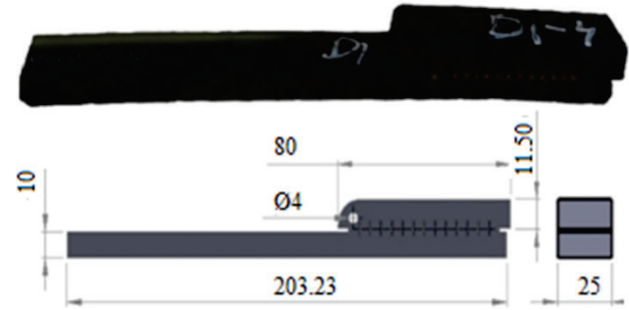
Ezme test düzeneği (The crush decohesion test assembly)
